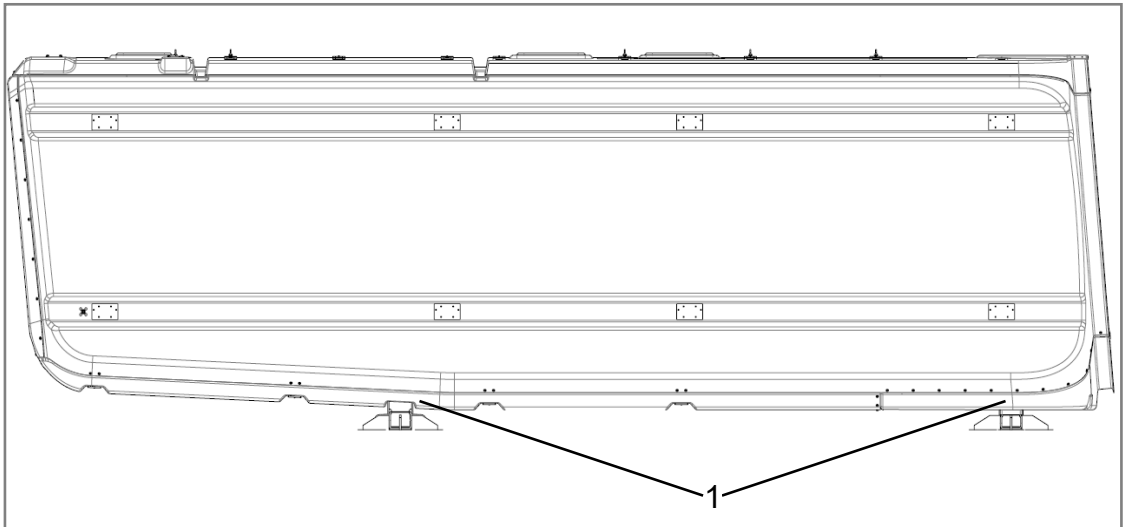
Maschinenhaus, Ansicht von rechts mit Transportfüßen (1)
